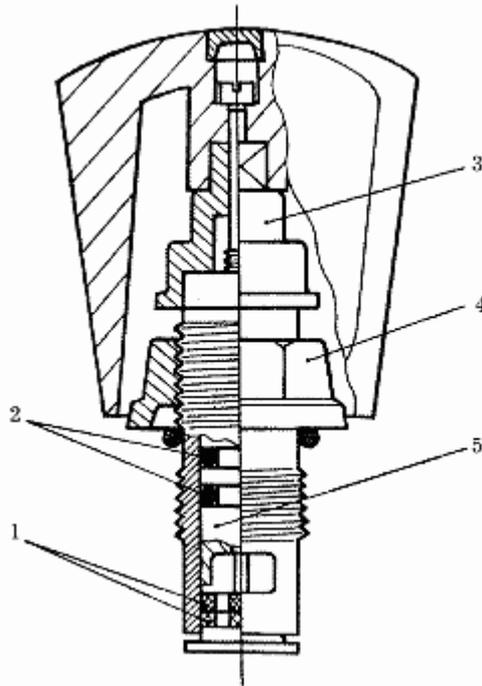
Головка крана с керамическими дисками: 1 – притертые керамические диски; 2 – уплотнительное кольцо; 3 – механизм поворота; 4 – регулирующая гайка; 5 – поворотный цилиндр из самосмазывающейся пластмассы.
